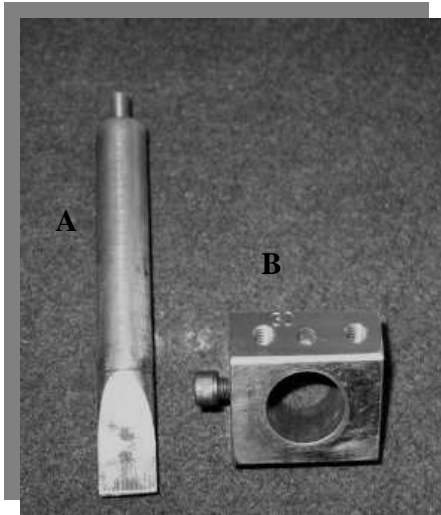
A) - Haste metálica que ficará em contato direto como dente; B) - Dispositivo metálico para adaptar o corpo-de-prova à máquina universal de ensaios.
